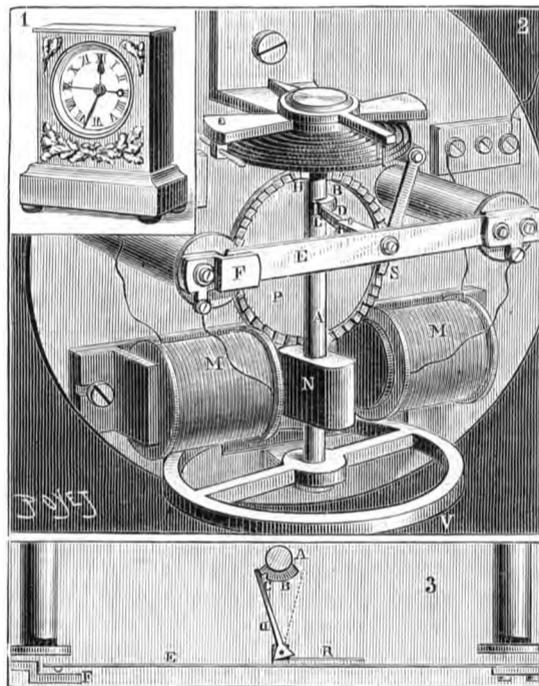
, 2 et 3. — Pendule électrique de M. Cauderay. — 1. Vue d'ensemble de la pendule. — 2. Mécanisme moteur. — 3. Détails de l'interrupteur.
